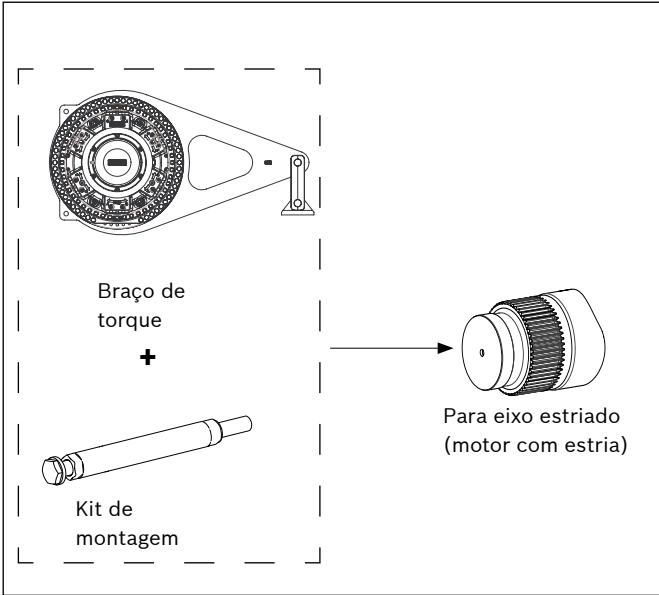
Montagem do braço de torque de uma terminação no eixo estriado, permitido apenas para CBm 2000 a CBm 4000 (não permitido para CBm 5000 a CBm 6000)
